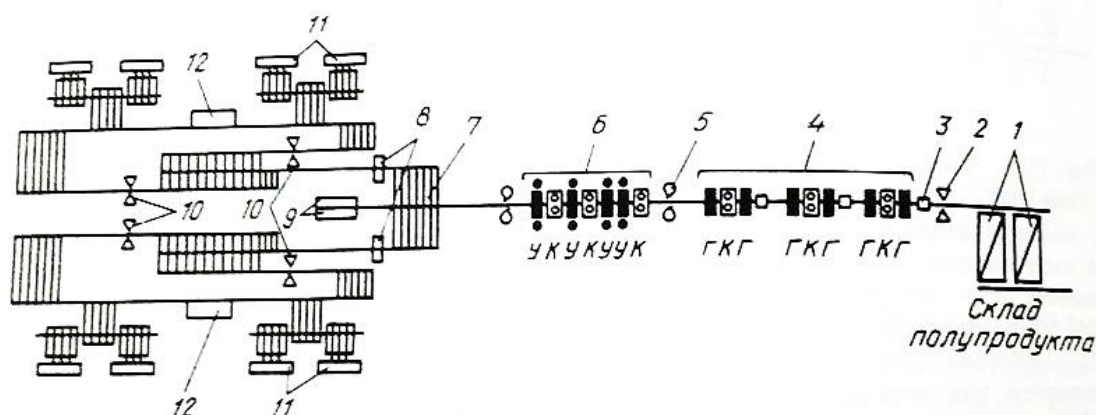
Схема расположения оборудования непрерывного [9] среднесортного стана 450:
